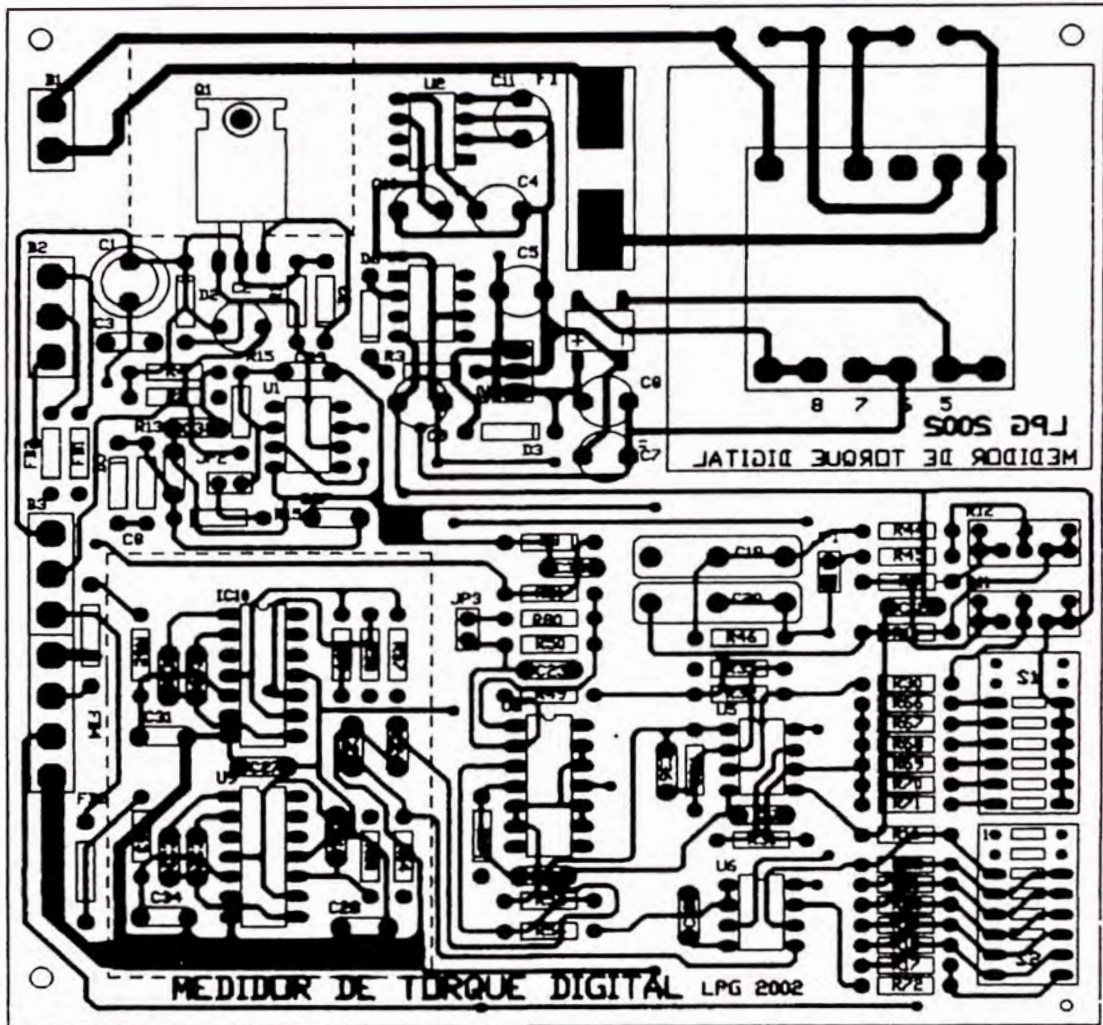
Circuito impreso: lado de la soldadura.
